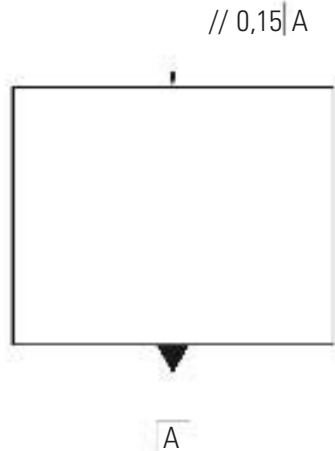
Unión del rectángulo de tolerancia sobre el elemento controlado en el eje.
